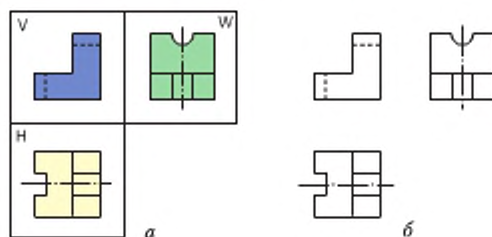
Креслення трьох проєкцій: а – прямокутні проєкції предмета; б – кресленник
